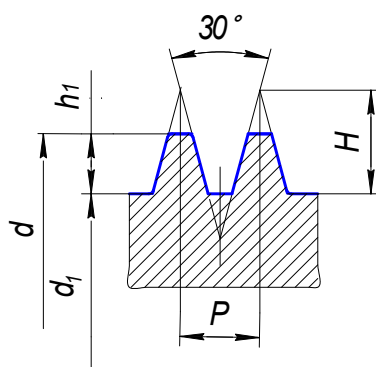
Профиль трапецеидальной цилиндрической резьбы
